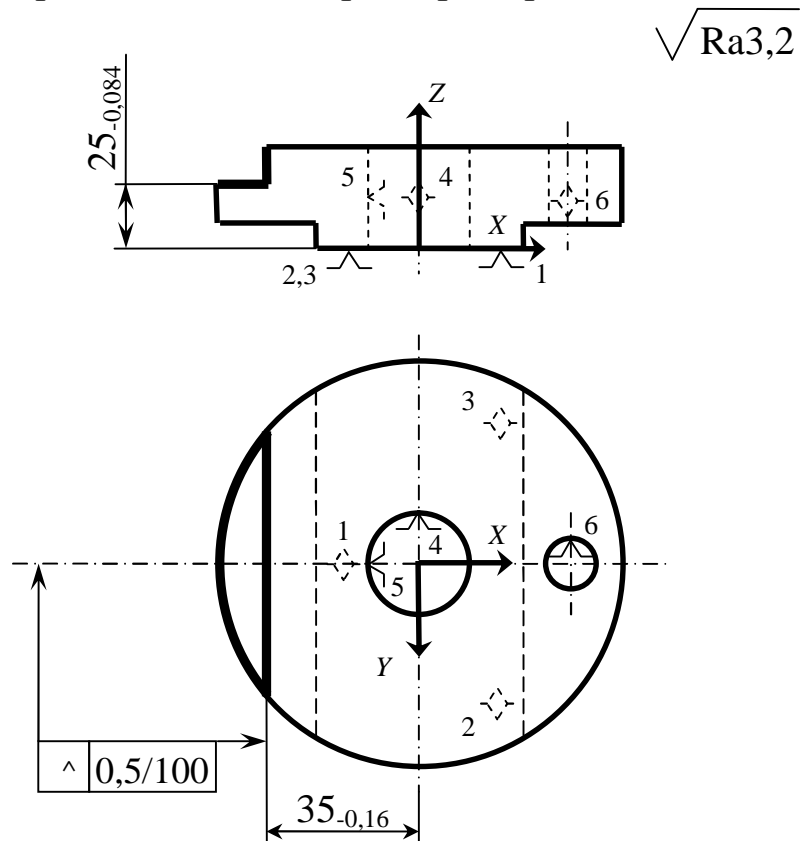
Операционный эскиз и схема базирования заготовки
